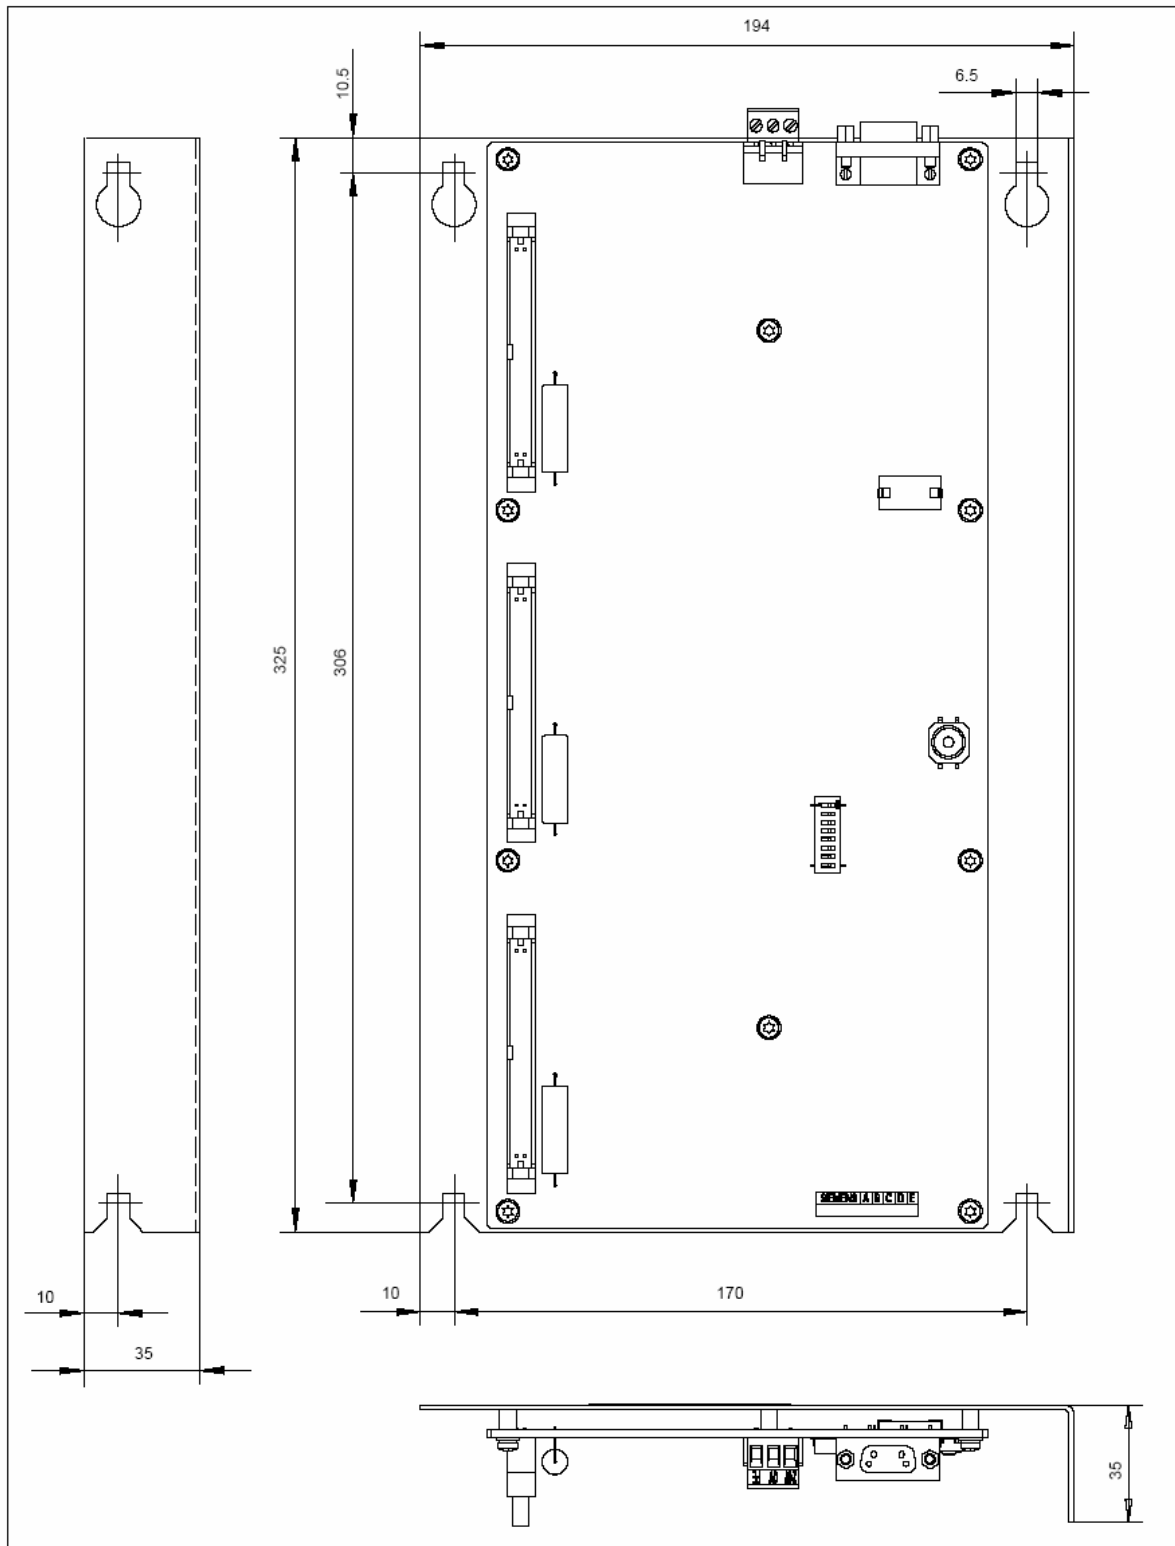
Габаритный чертёж: I/O Module PP72/48
